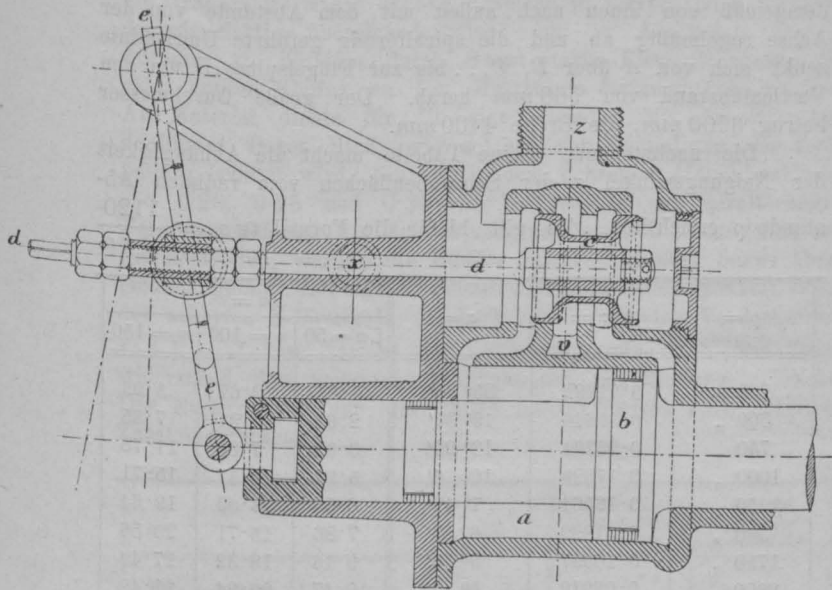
Detail der Cylinder-Steuerung der Bohrmaschine.
